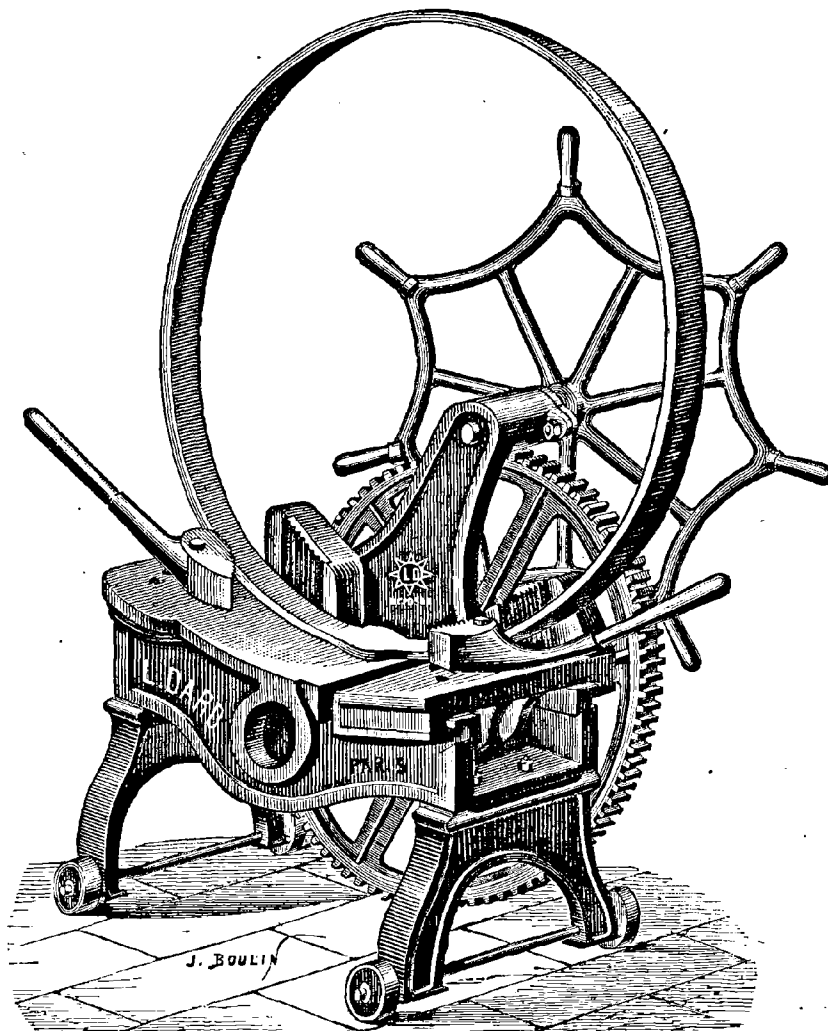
Machine à souder et à refouler les cercles de roues de M. Dard.
